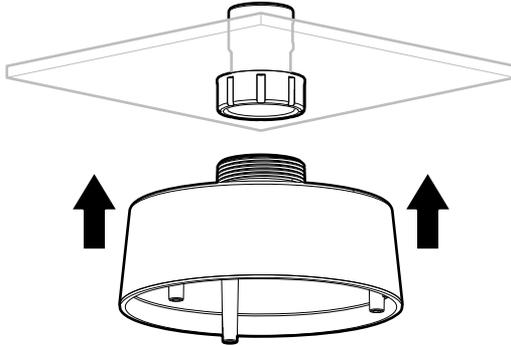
Установка подвесного крепления: модель с защитой от внешних воздействий/вандализма
